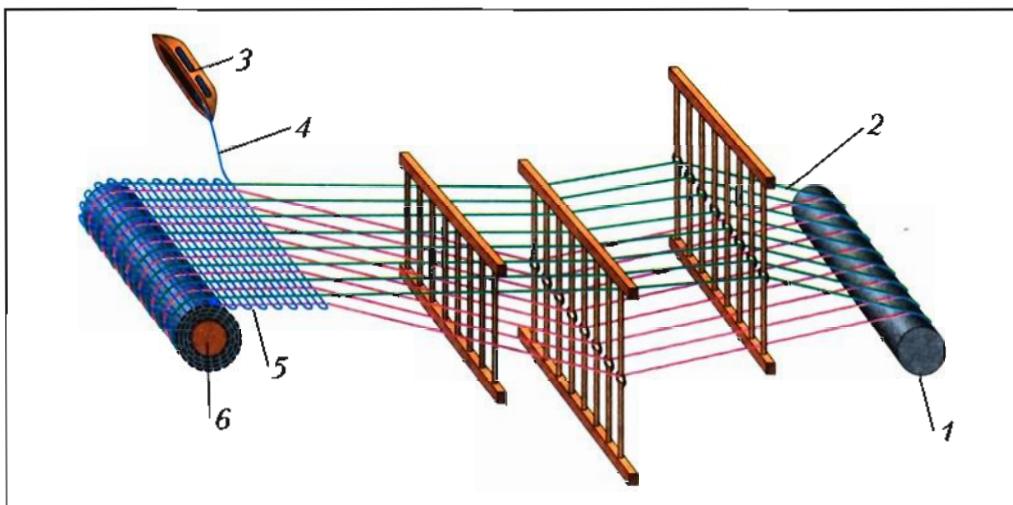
Процесс изготовления ткани на ткацком станке: 1 – навой; 2 – нити основы; 3 – челнок; 4 – нити утка; 5 – кромка; 6 – товарный валик
